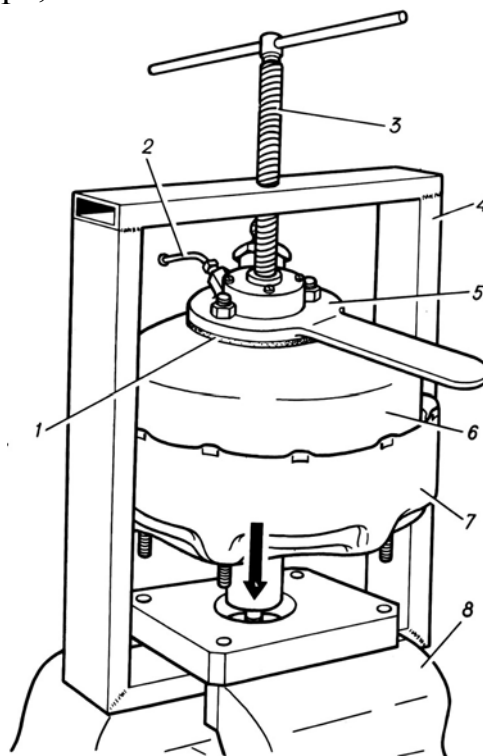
Приспособление для разборки и сборки усилителя: 1 - прокладка; 2 - трубка; 3 - винт; 4 - приспособление; 5 - заглушка; 6 - крышка; 7 - корпус; 8 - тиски
